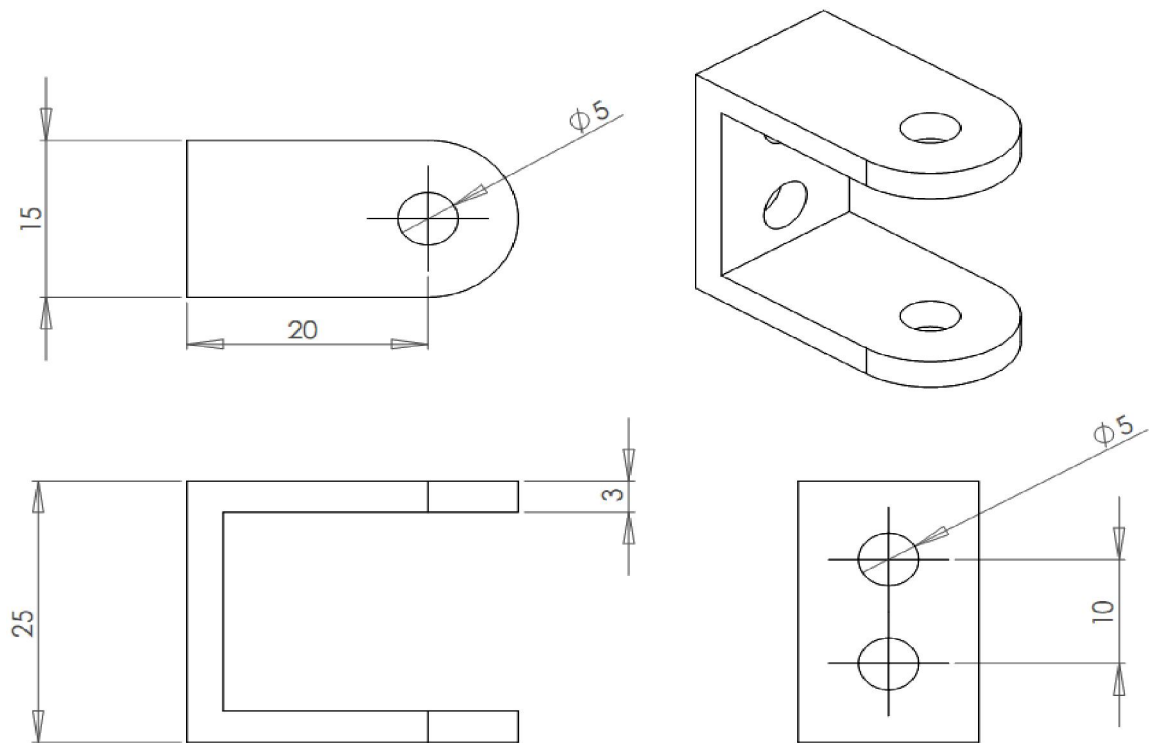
Dimensões finais do suporte do braço de direção (em mm)
